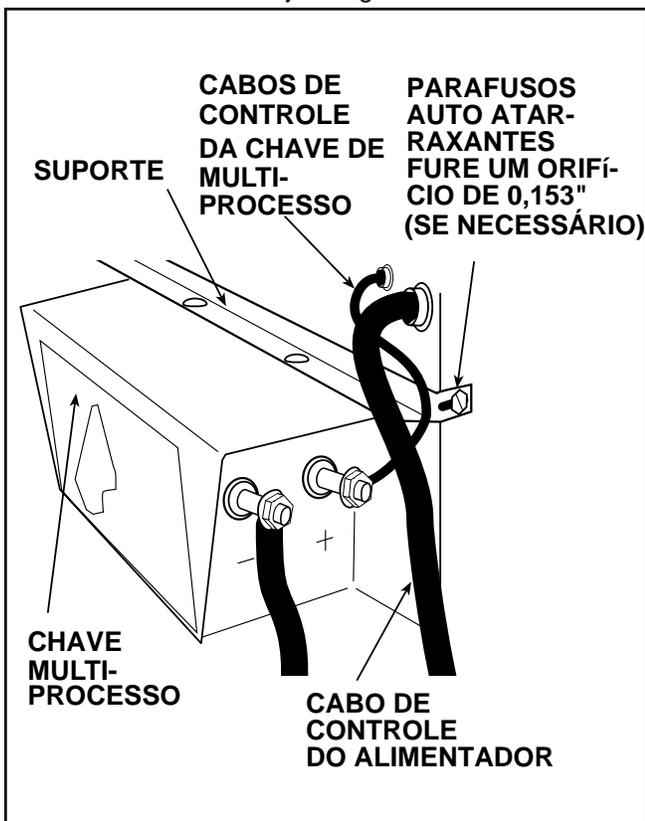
FIXAÇÃO DO SUPORTE DA CHAVE MULTI-PROCESSO.
